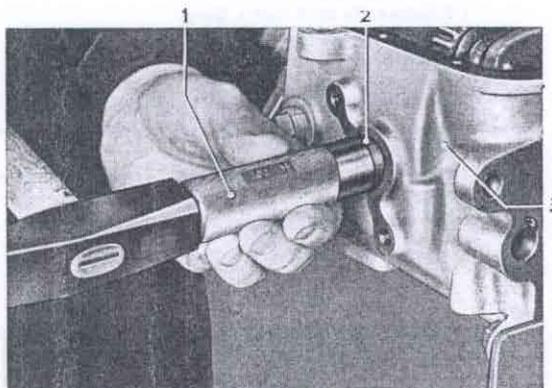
Simmerring für Getriebeschaltwelle in Getriebegehäuse einschlagen
